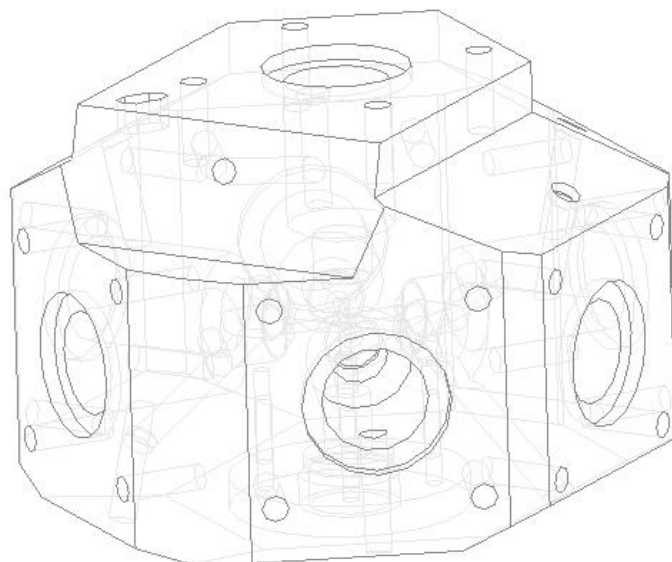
Загальний вигляд «корпусу ЦФ 8.171.644»
